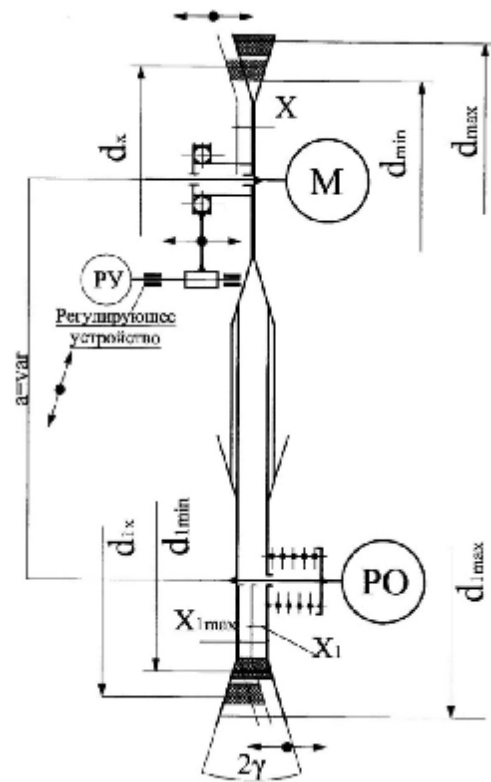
Вариатор с двумя раздвижными шкивами и несимметричным регулированием.
